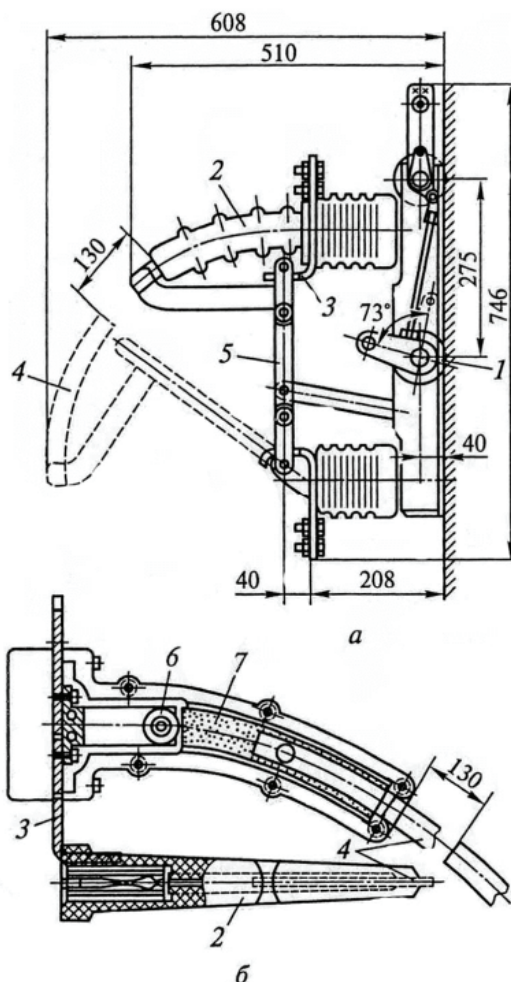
Дугогасящая камера выключателя нагрузки ВН [3, с.86]: а — общий вид; б — дугогасительная камера; 1 — вал привода; 2 — дугогасительная камера; 3 — главный неподвижный контакт; 4 — подвижный дугогасительный контакт; 5 — главный подвижный контакт-нож; 6 — неподвижный дугогасительный контакт; 7 — газогенерирующие вкладыши.
